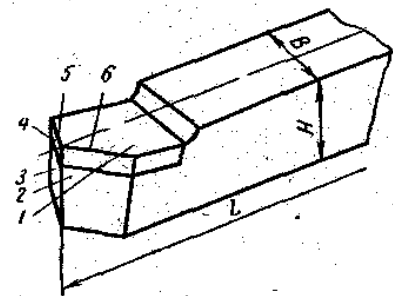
Элементы рабочей части резца: 1 — передняя поверхность, 2 — главная задняя поверхность, 3 — вспомогательная задняя поверхность, 4 — вершина резца, 5 — вспомогательная режущая кромка, 6 — главная режущая кромка
